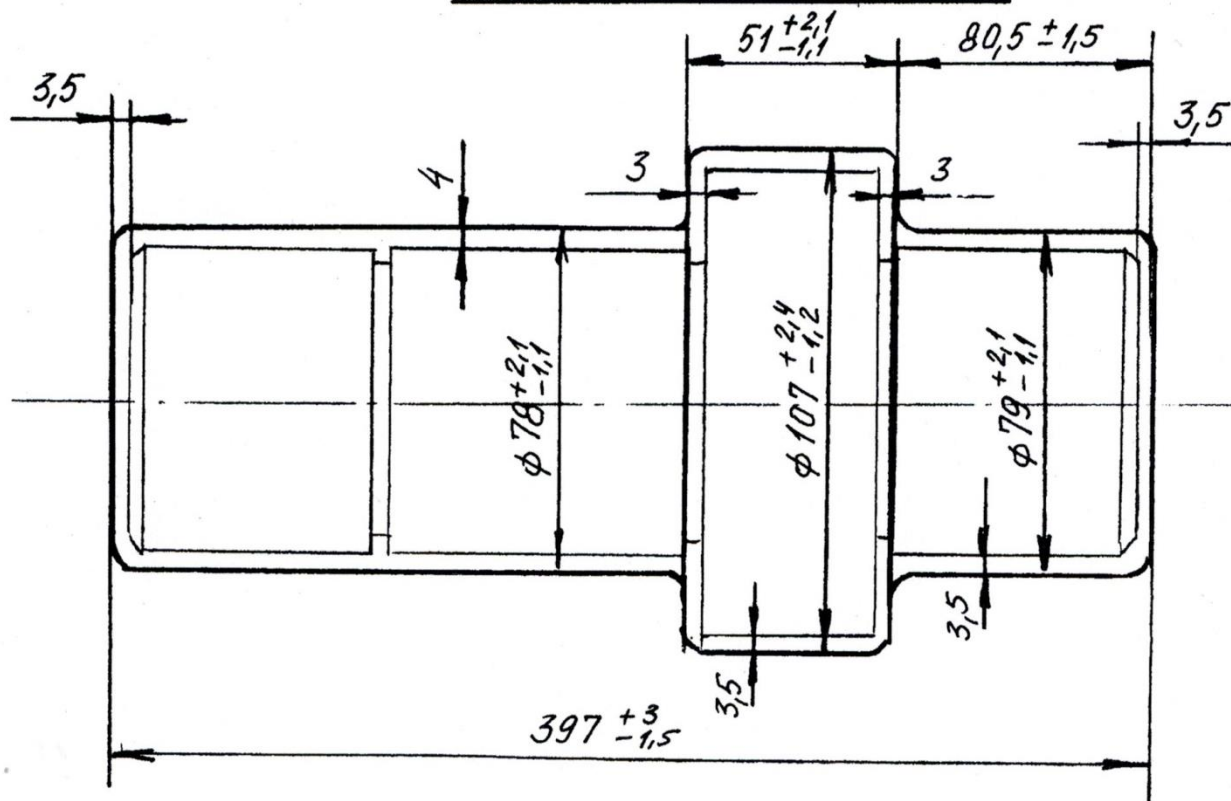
заготовка – поковка, штампованная на ГКМ.
